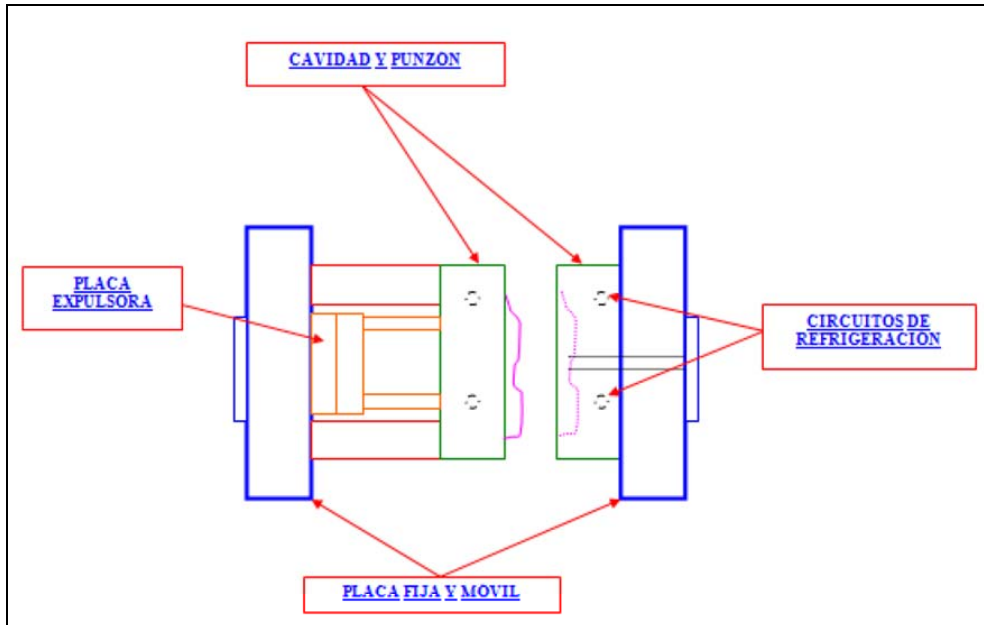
Partes del molde dedicadas a la inyección.
